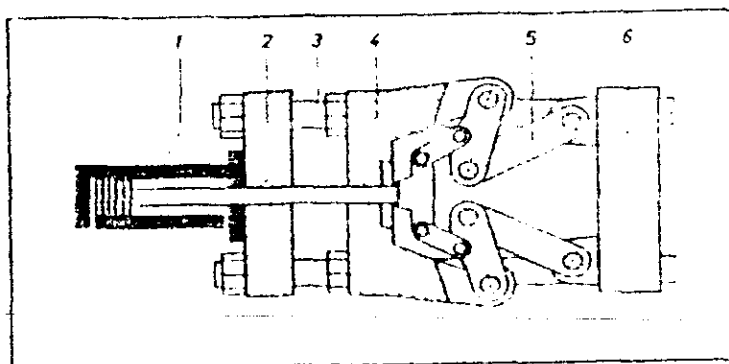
Esta construcción utiliza una placa intermedia, pero su sistema de palancas articuladas es accionado por un cilindro hidráulico largo, dispuesto frente a la placa frontal. El desplazamiento de la placa de cierre (posición extendida del sistema de palancas articuladas) tiene lugar por desplazamiento de posición de la placa
